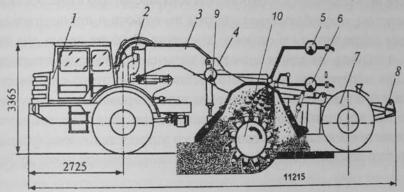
Конструктивная схема рециклера на агрегатах скрепера МоАЗ-6014: 1 — одноосный тягач; 2 — седельно-сцепное устройство; 3 — тяговая рама; 4 — гидроцилиндр; 5 — насос подачи вяжущего (битумной эмульсии); 6 — насос подачи воды; 7 — заднее колесо; 8 — буфер; 9 — устройство подачи активирующей добавки; 10 — фрезерный барабан
